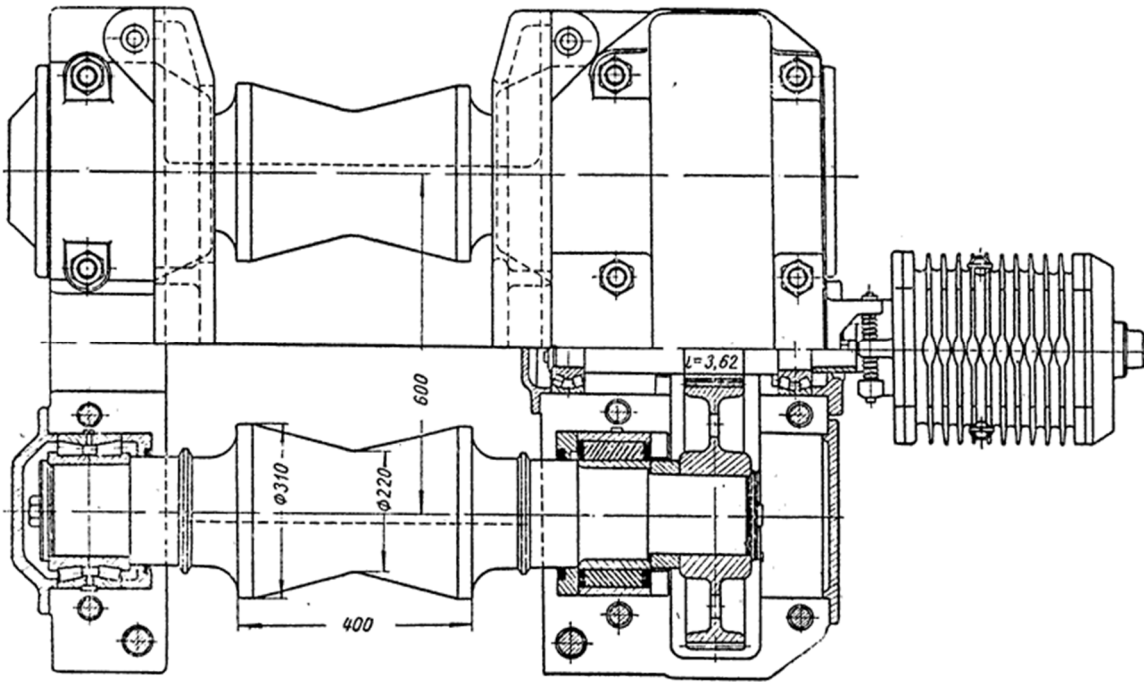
Сварений привід рольганга з двигуном, який має порожнистий вал
